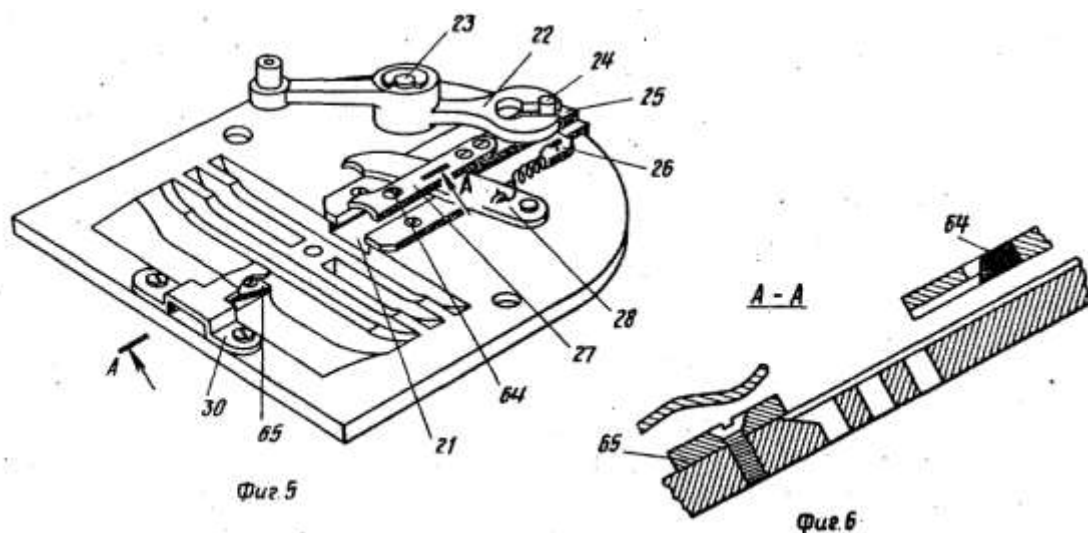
Варіант виконання ножів із пластинками із твердого сплаву та розріз А-А.
